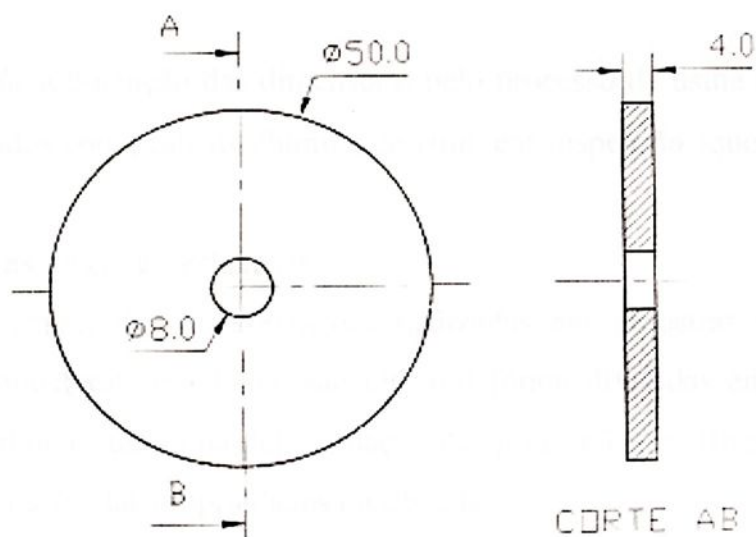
Geometria e dimensões do disco de C/C (mm).
